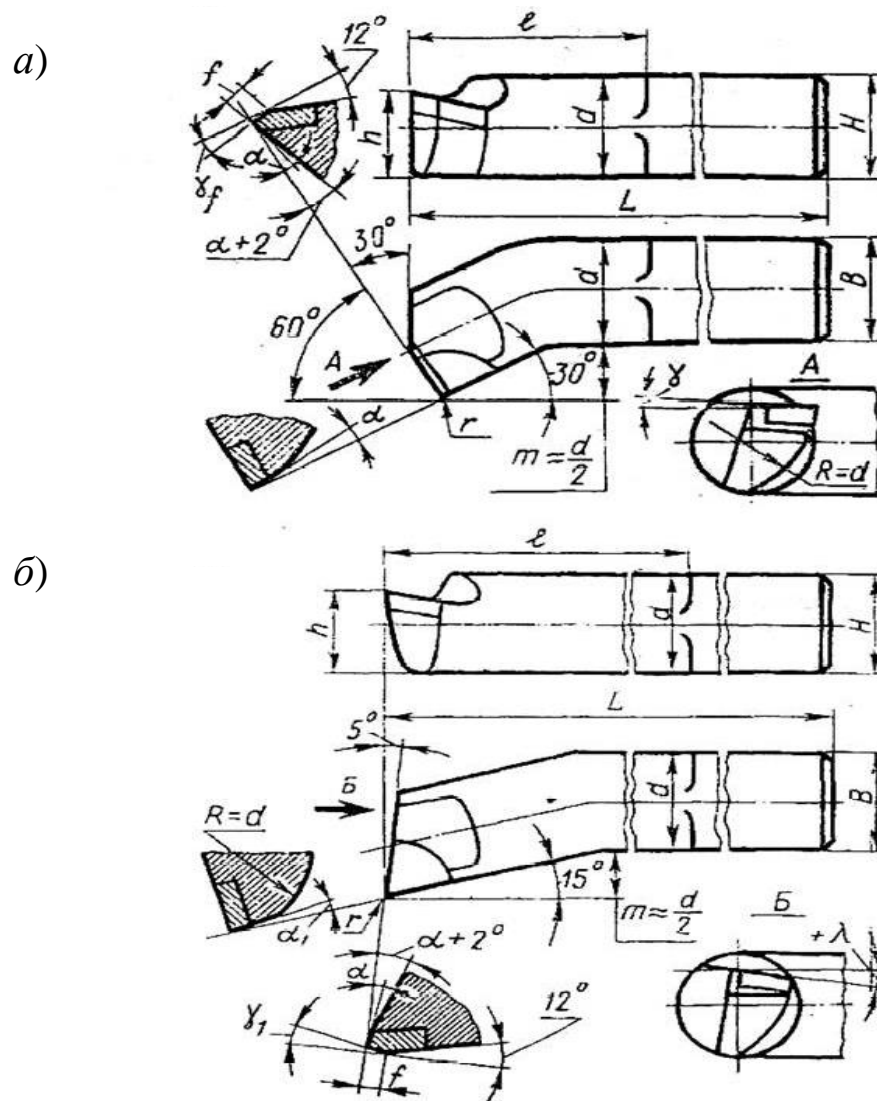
Токарные расточные резцы: *а* – для обработки сквозных отверстий; *б* – для обработки глухих и ступенчатых отверстий
